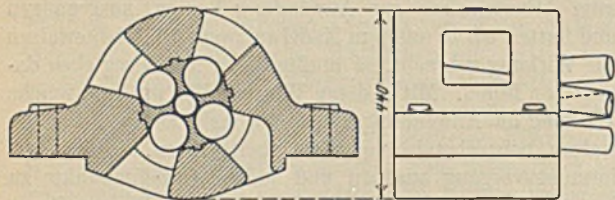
Streck-schrägwalzwerk, Bauart Kocks.
